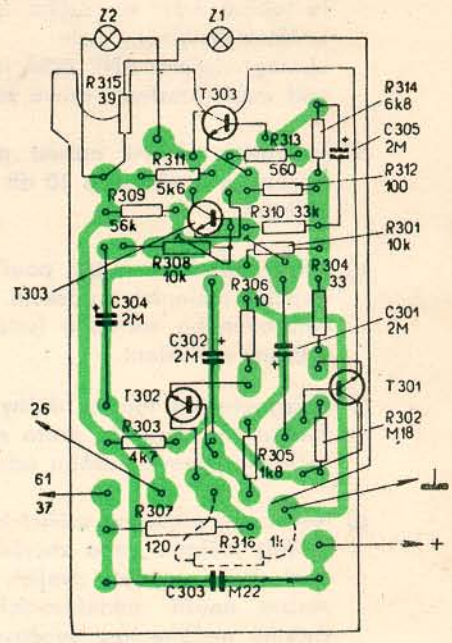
Zapojení desky s plošnými spoji (ze strany součástek)
